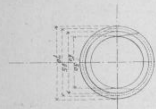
Vue par bout de la garniture *oo* en métal blanc, en 2 pièces.
